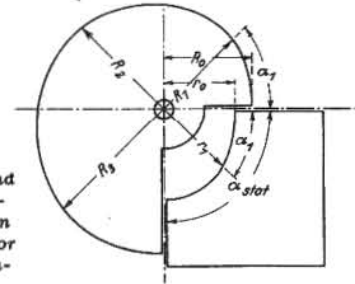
Rotor- und Stator-Plattenschnitt für einen Drehkondensator mit einem Drehwinkel = 270°
